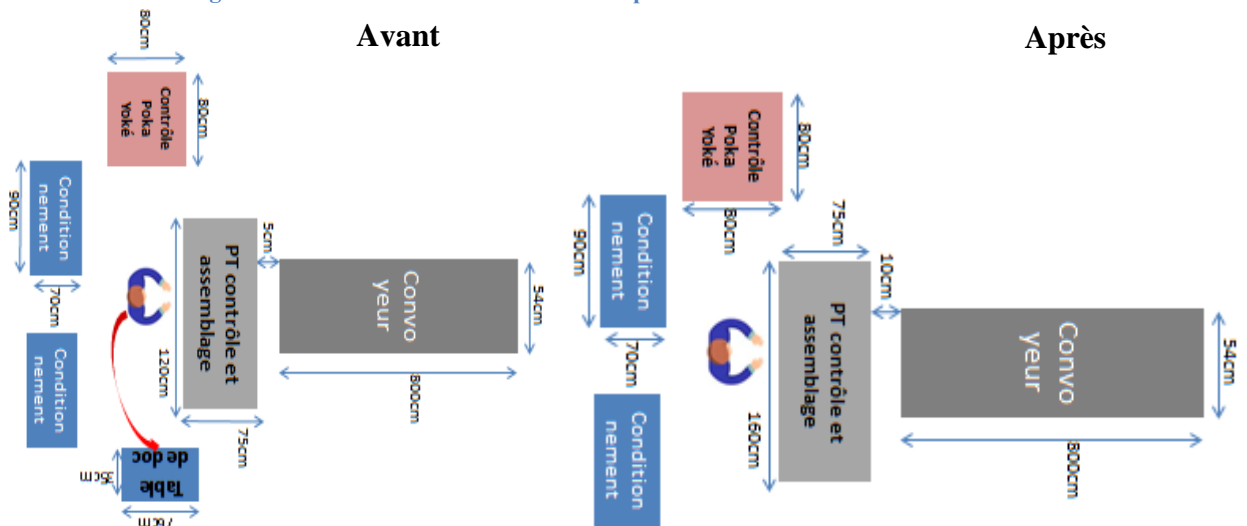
LAYOUT du A Pillar avant et après l'installation du nouveau PT
